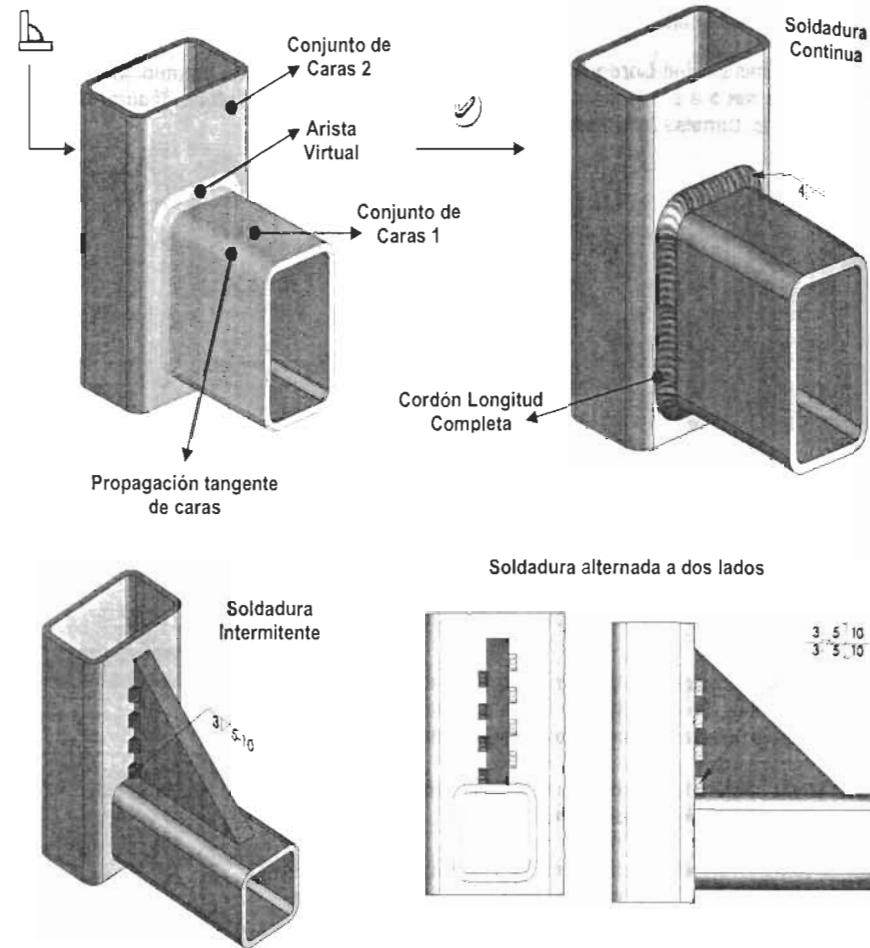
Ejemplos de Cordones de soldadura de redondeo.
